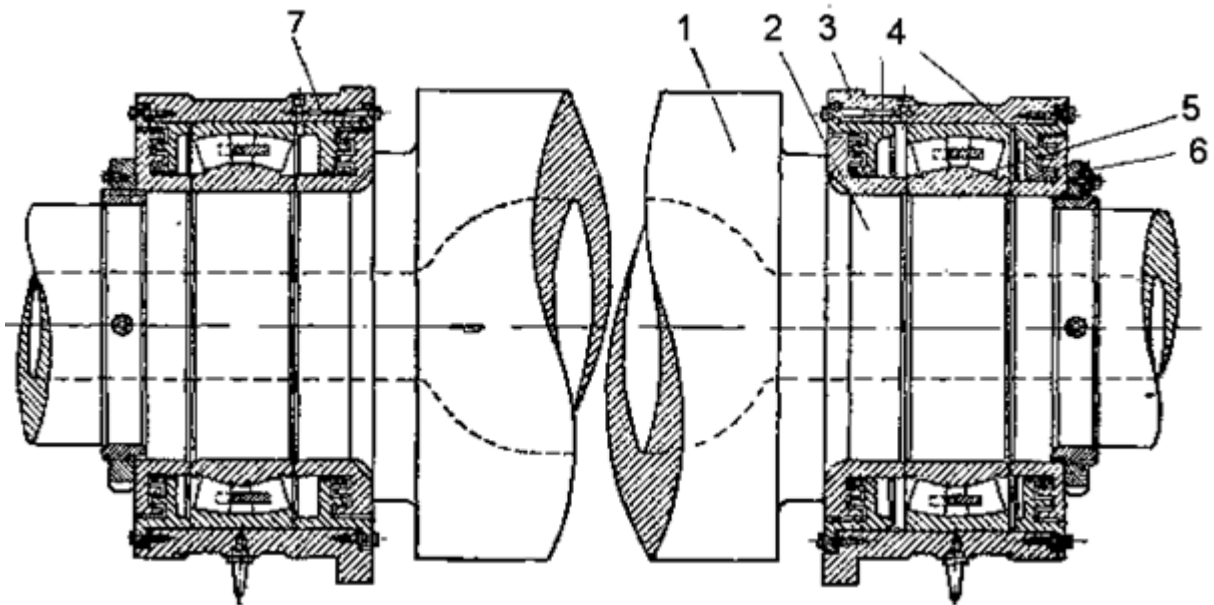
Вузол валкових підшипників: 1 – робоча поверхня валка; 2 – шийка валка; 3 – корпус підшипника; 4 – лабіринтові ущільнення; 5 – підшипник; 6 – стопорне кільце; 7 – канали для мастила
